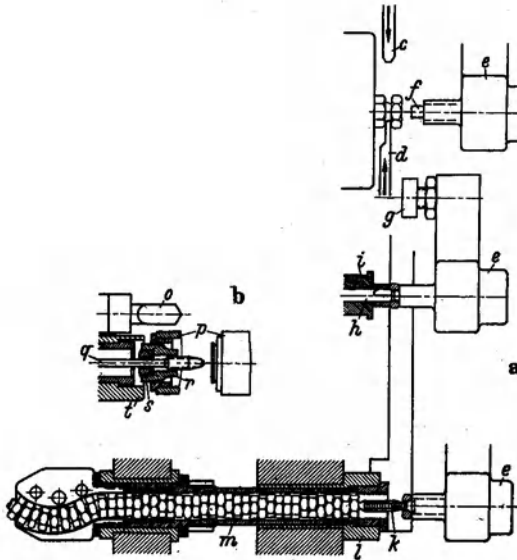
Bearbeitung von Sechskantmuttern mit Mutternschneideinrichtung. *a* Bohrer mit Senker *b*; *c* Einstechstahl; *d* Abstechstahl; *e* Greifarm mit Aufnahmedorn *f*, welcher federnd in einer Hülse sitzt; *g* Anschlag; *h* Senker für die hintere Seite, besonders angetrieben; *i* Lagerbüchse für den Senker; *k* Gewindebohrer; *l* vordere Lagerbüchse; *m* Gewindebohrerspindel, besonders angetrieben. Abb. 39b. Senker und Gewindebohrereinrichtung für Rundmuttern. *o* Senker; *p* Greifarm; *q* Gewindebohrer; *r* Spannzange im Greifarm; *s* Arbeitsstück; *t* vordere Lagerbüchse der Gewindebohrerspindel.
